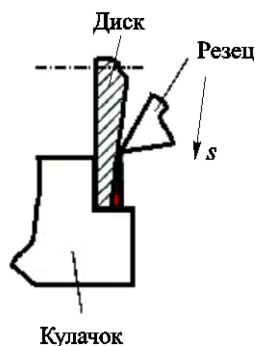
Подрезка торца диска при закреплении в трехкулачковом патроне (заливкой отмечена опасная зона при обработке; s — направление подачи инструмента)
